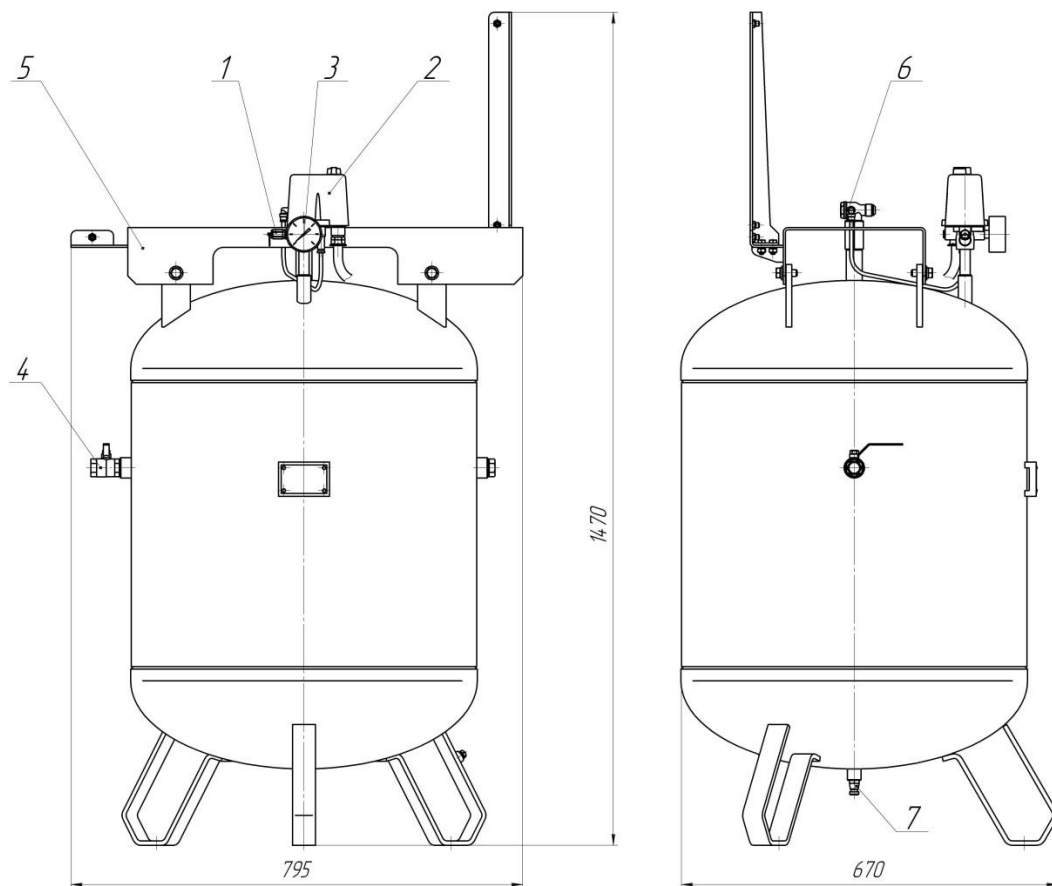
Резервуар установки компрессорной, модель К-6:
